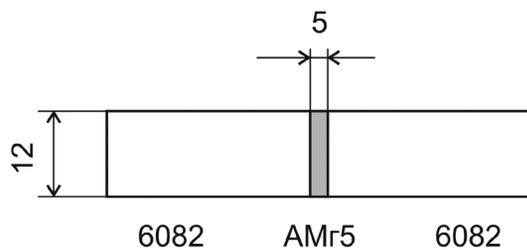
Условная схема поперечного сечения образца сварного шва при сварке встык пластин из сплавов АМг5 и 6082
